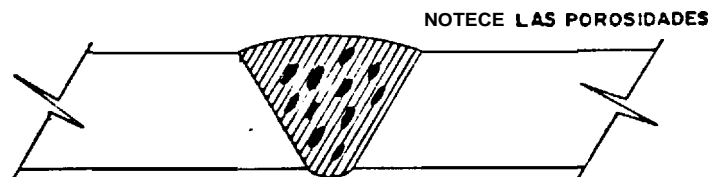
CONDICION DE POROSIDAD (REF. AWS WELDING' HANDBOOK). Ref. 7)
